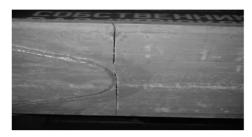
Трещина на сварном шве накладки усиления боковой балки
